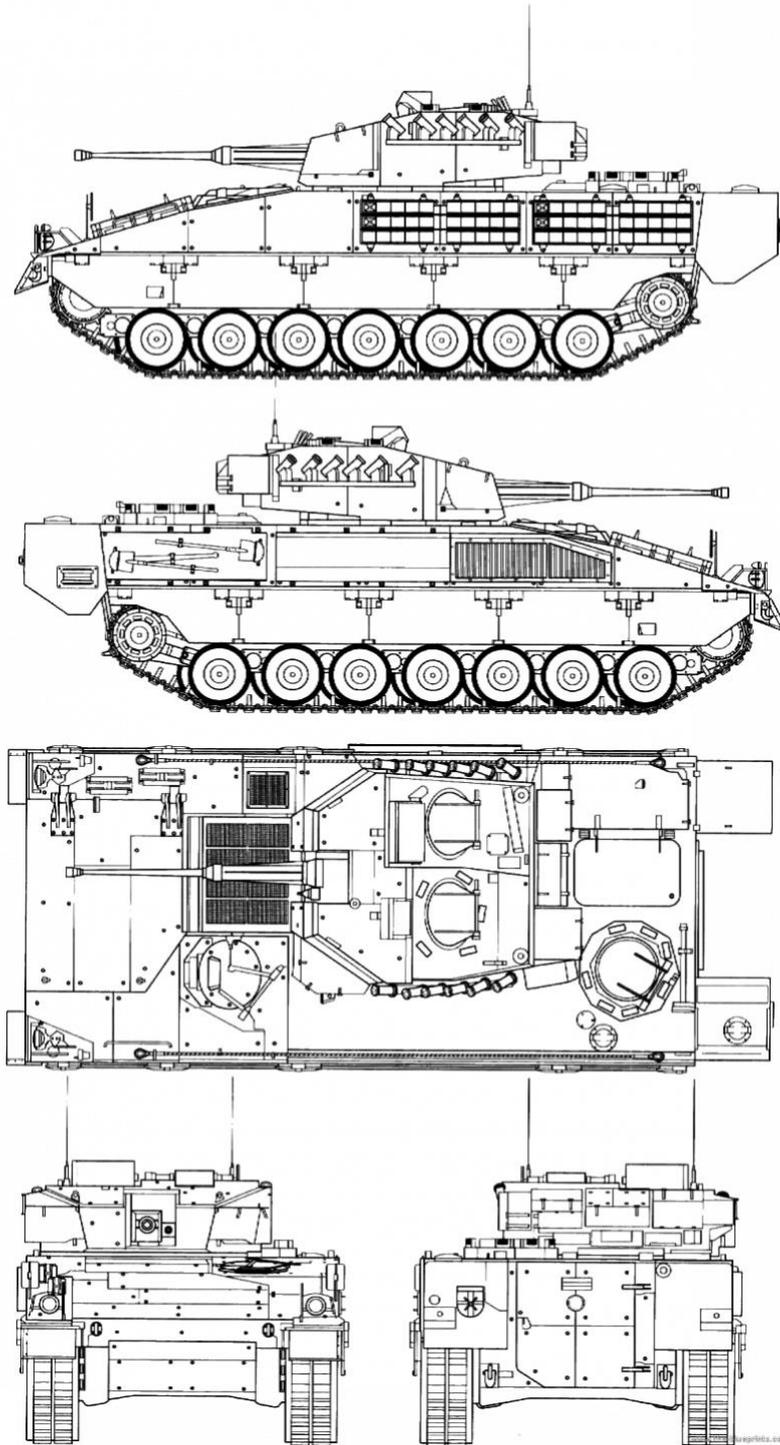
Perfil, planta y alzado del VCI Pizarro. Fuente [24].
